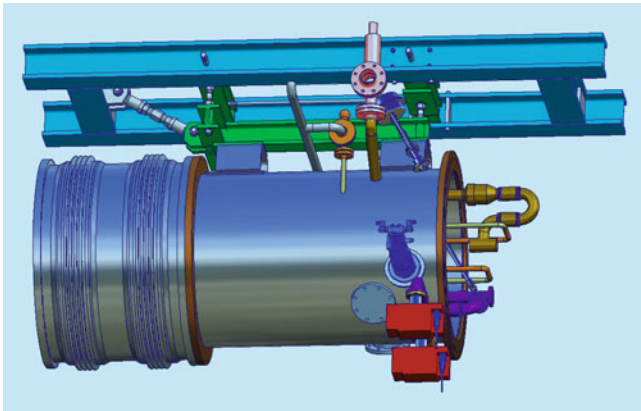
String-Connection-Box SCB mit Deckenanbindung
